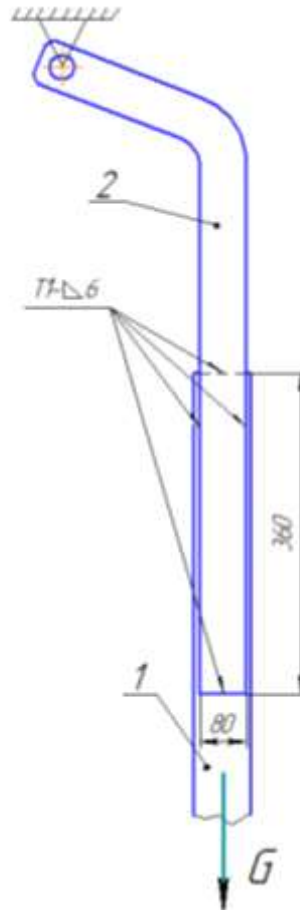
Розрахункова схема зварного з'єднання
